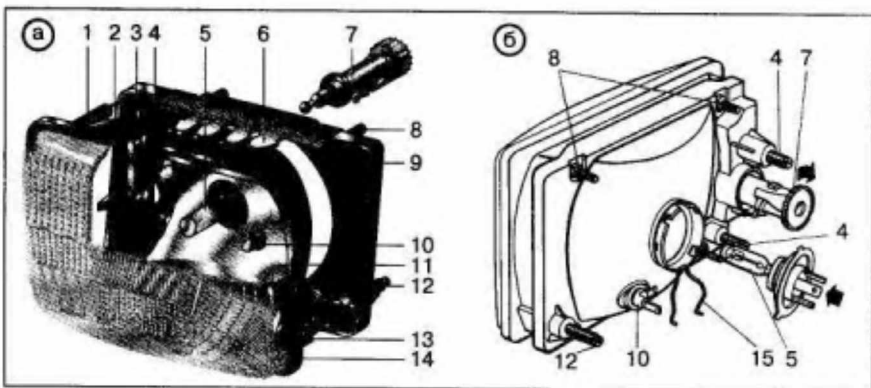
Прямоугольная фара с галогенной лампой: а — устройство; б — положение ручек регулирования; 1 — стяжная пружина; 2 — верхний держатель отражателя; 3 — рычаг; 4 — винт регулирования в вертикальной плоскости; 5 — галогенная лампа; б — кронштейн; 7 — установочный винт; 8 — винт крепления фары; 9 — корпус; 10 — лампа габаритного огня; 11 — отражатель; 12 — винт регулирования в горизонтальной плоскости; 13 — нижний держатель отражателя; 14 — расцеиватель; 15 — пружинная защелка
